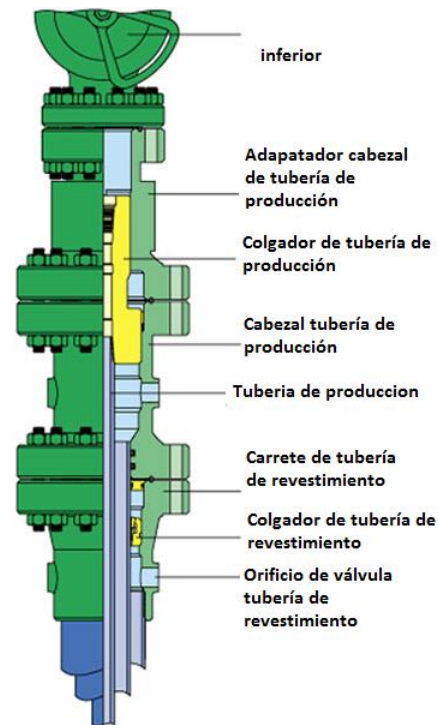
Componentes de cabezal de pozo. Fuente: Glosario técnico de Schlumberger.
